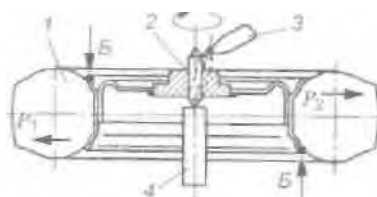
Динамическая балансировка колеса: 1 — колесо; 2 — приспособление; 3 — мел; 4 — опора
